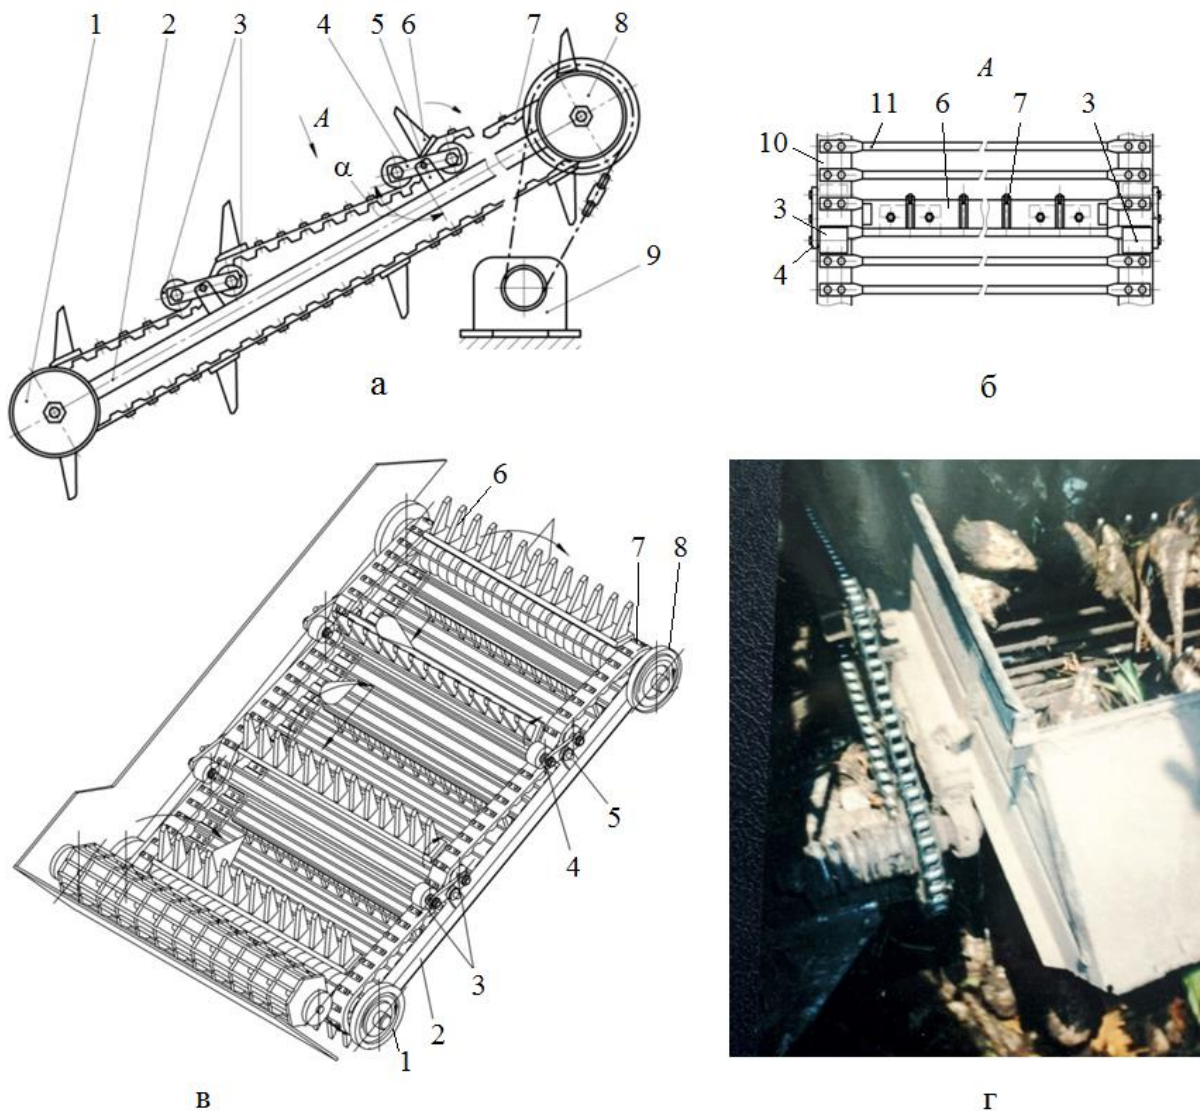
Конструктивна схема скребкового транспортера-сепаратора коренеплодів: а – загальний вигляд; б – вид по А; в – вигляд у форматі 3D; г – загальний вигляд транспортера-сепаратора
